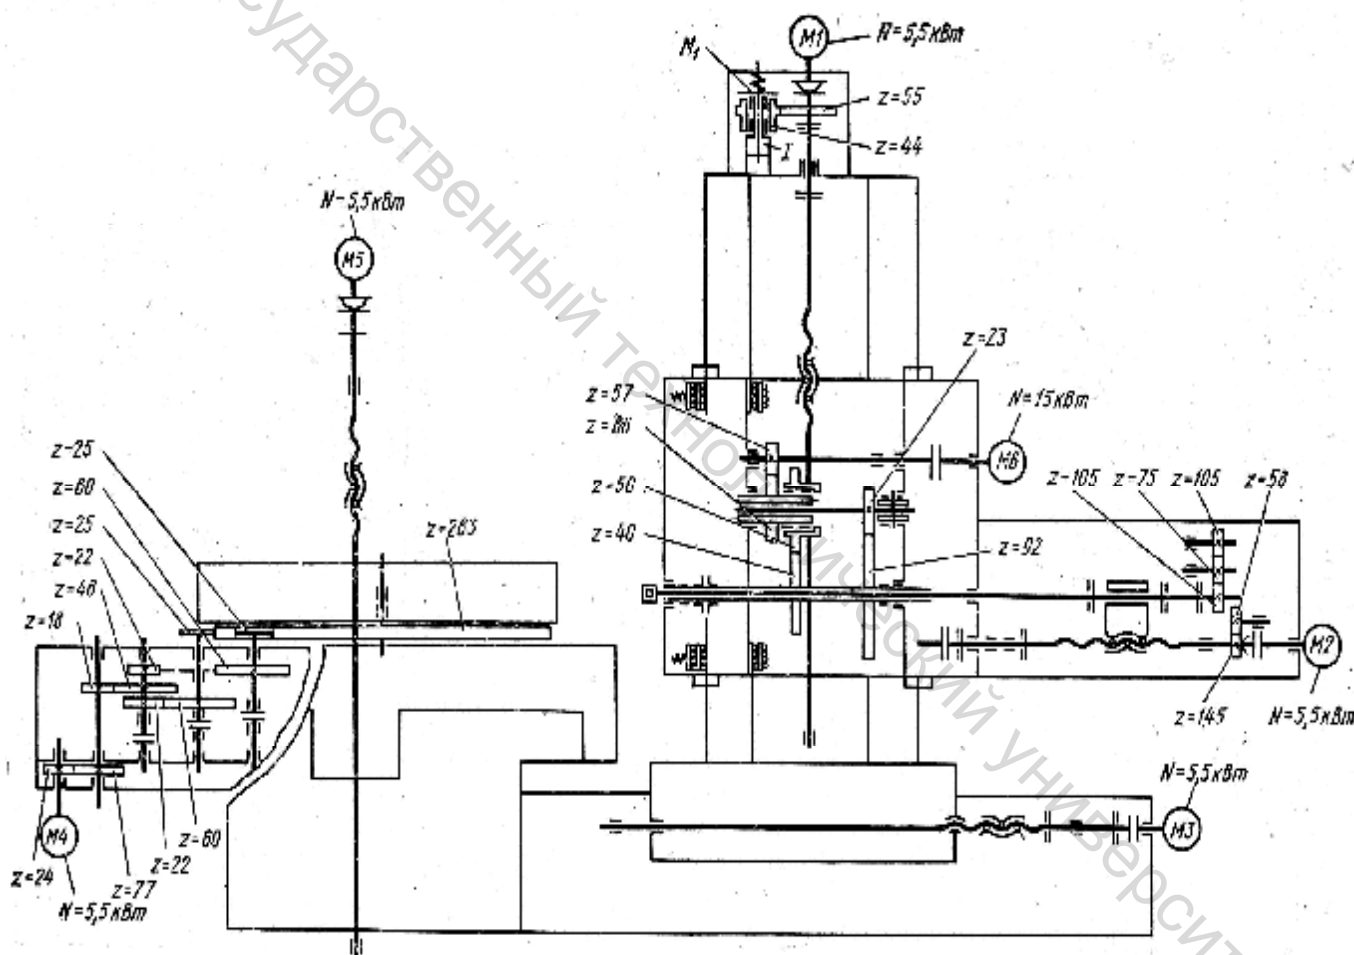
Кинематическая схема станка мод. 2623ПМФ-4
